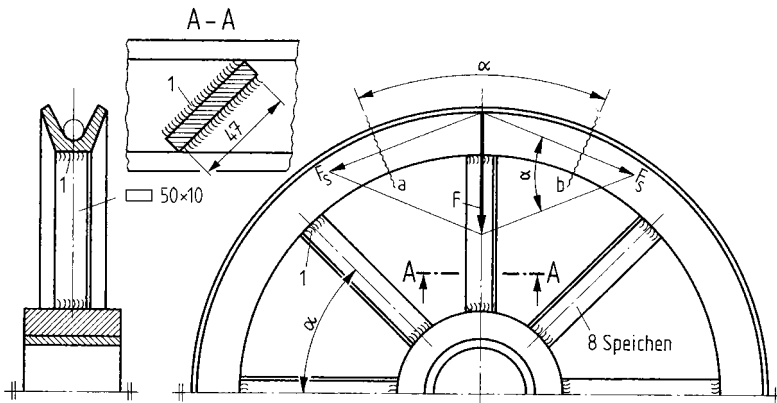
Seilrolle mit eingeschweißten Speichen
